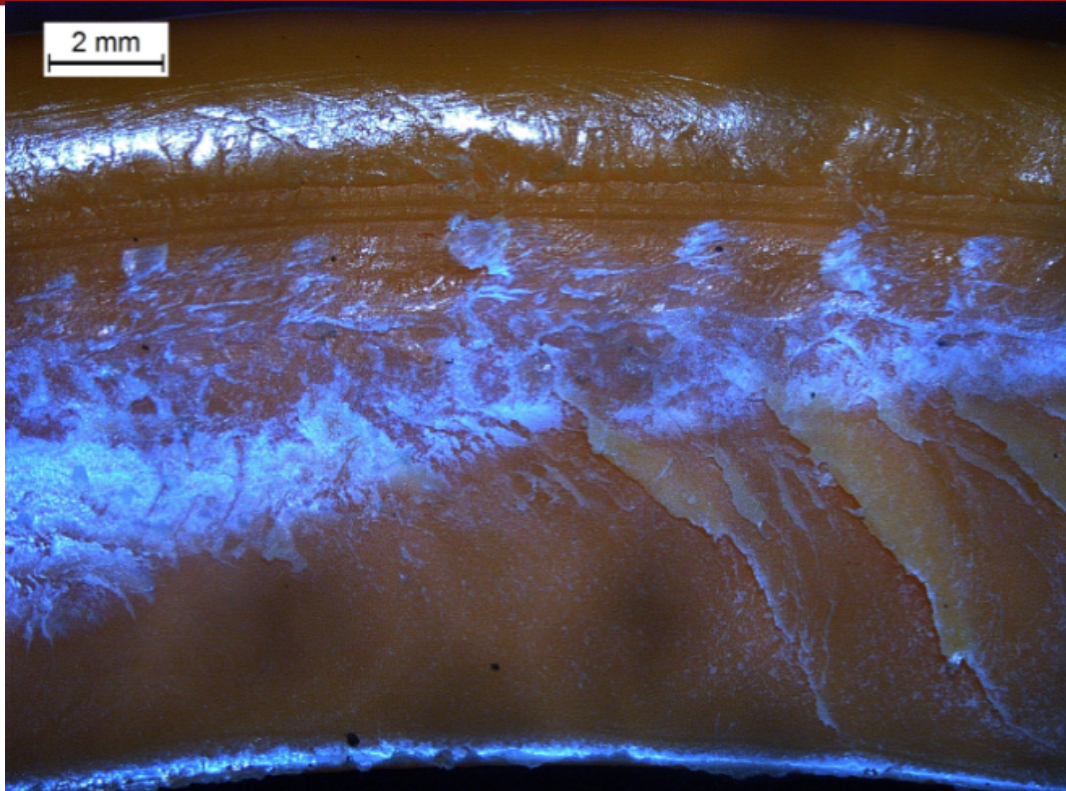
Superficie de fractura soldadura a 600 RPM, probeta 2000-2
